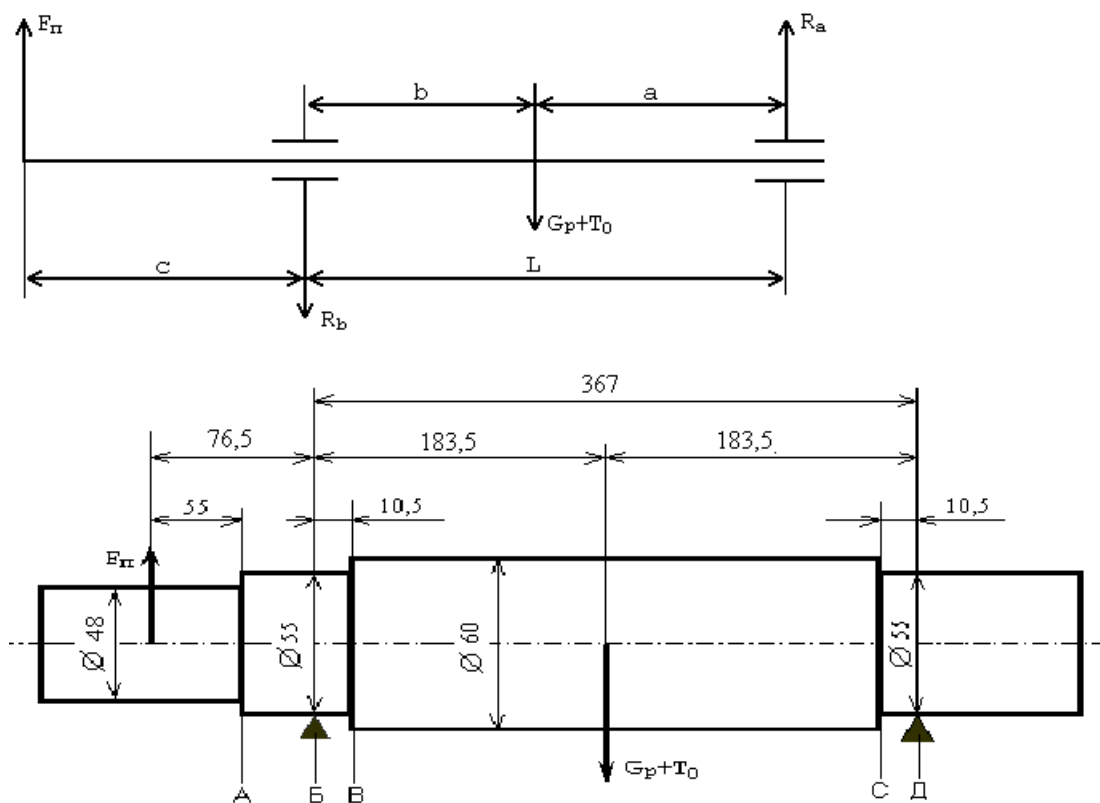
Конструкция и основные размеры вала для механического расчёта.
